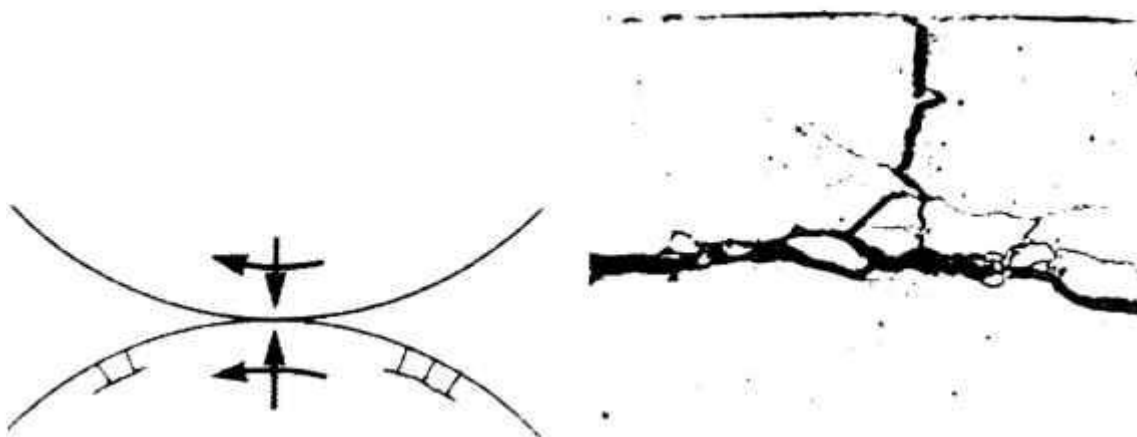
Apresenta trincas de fadiga paralela e perpendiculares à superfície [18]
